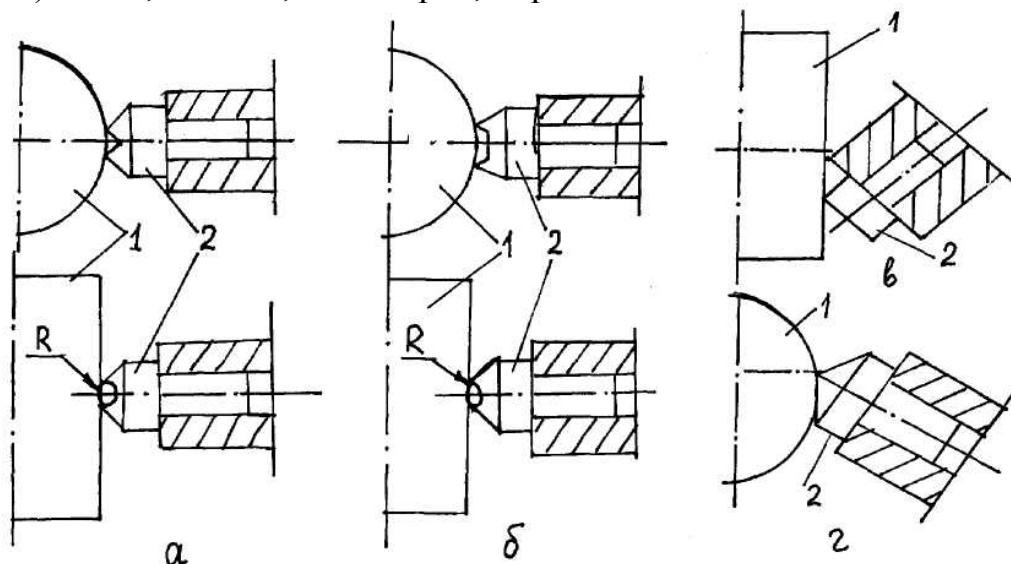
Схема установок выглаживателей при обработке цилиндрической поверхности: а – сферическая форма заточки, б – цилиндрическая, в – тороидальная, г – коническая; 1 – обрабатываемая поверхность, 2 - заточка
